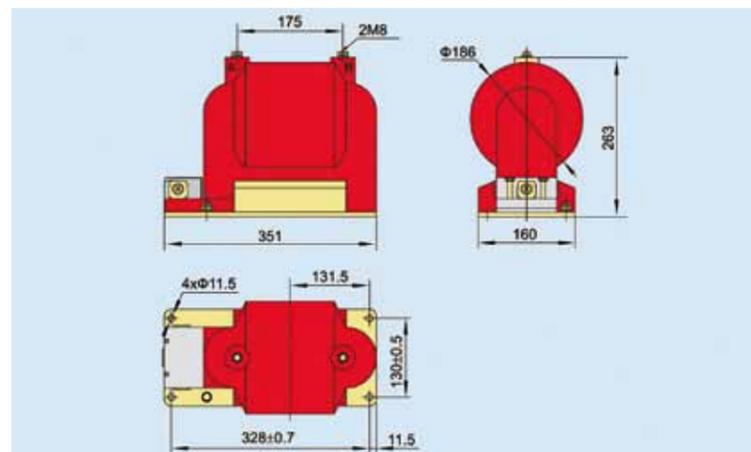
Внешний вид и размеры трансформатора напряжения JDZ9-10
